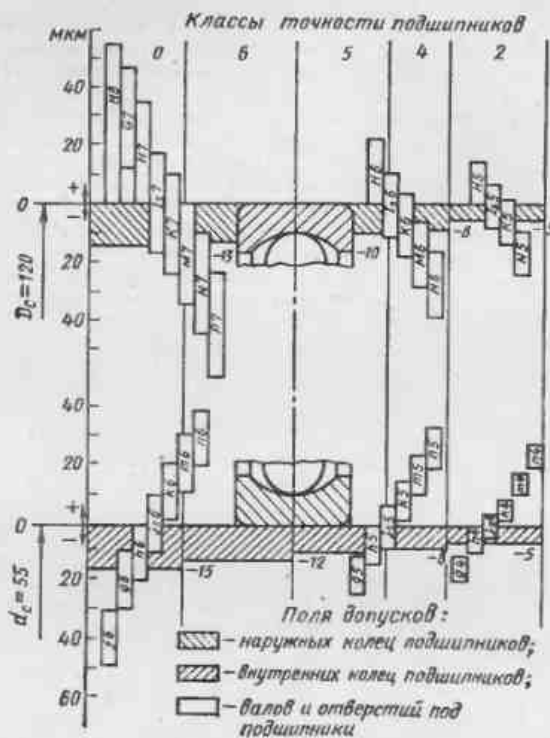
Схемы расположения полей допусков колец подшипников качения, валов и отверстий в корпусах для подшипников с  $d_c = 55$  мм,  $D = 120$  мм
